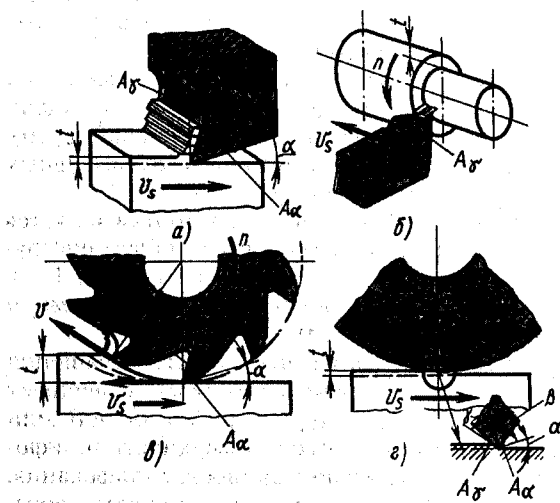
Рабочая часть режущего инструмента и движения в процессе обработки резанием: а — строгание, б — обтачивание, в — фрезерование, з — шлифование;  $A_\gamma$  и  $A_\alpha$  — передняя и задняя поверхности,  $v$  и  $v_s$  — скорости главного движения резания и движения подачи,  $n$  — частота вращения заготовки или инструмента;  $t$  — глубина резания,  $\gamma$  — передний угол,  $\alpha$  — задний угол,  $\beta$  — угол заострения
